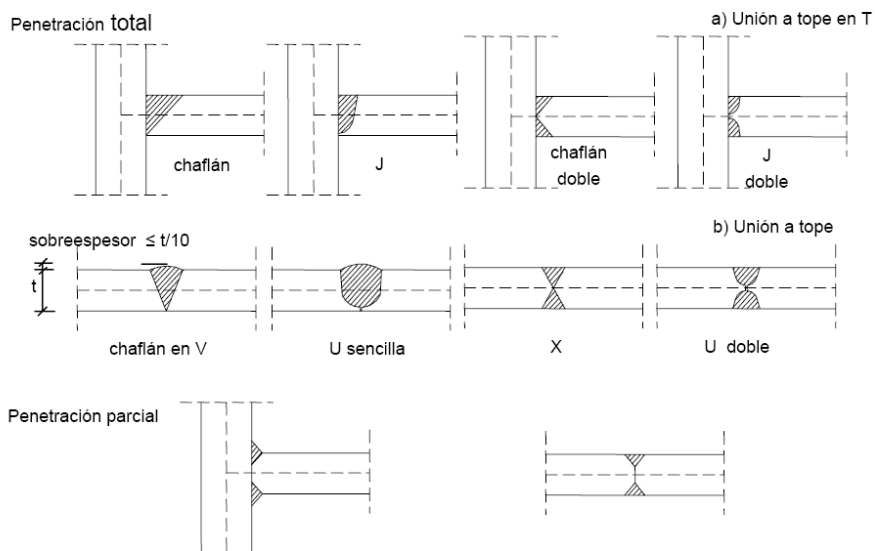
Soldadura a tope y formas de preparación
